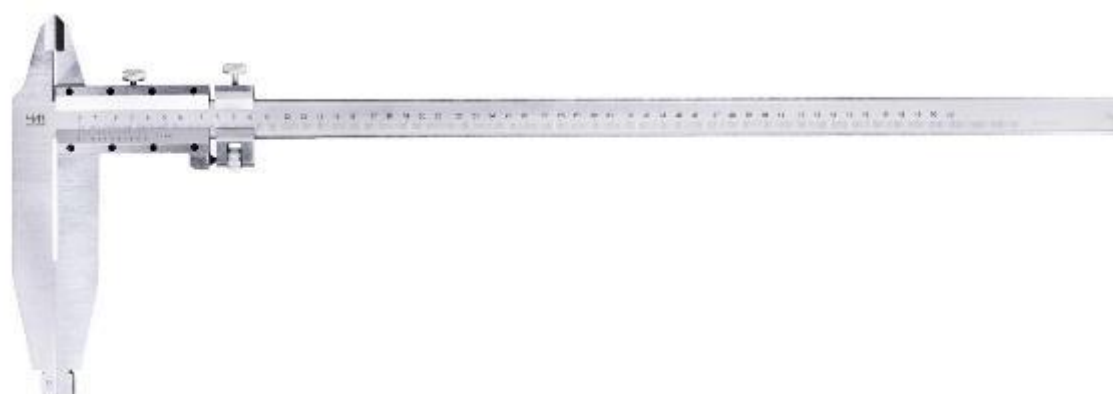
Общий вид штангенциркулей ШЦ-II
